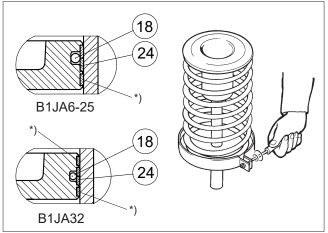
Serrage des joints de piston à l'aide d'un anneau de serrage
